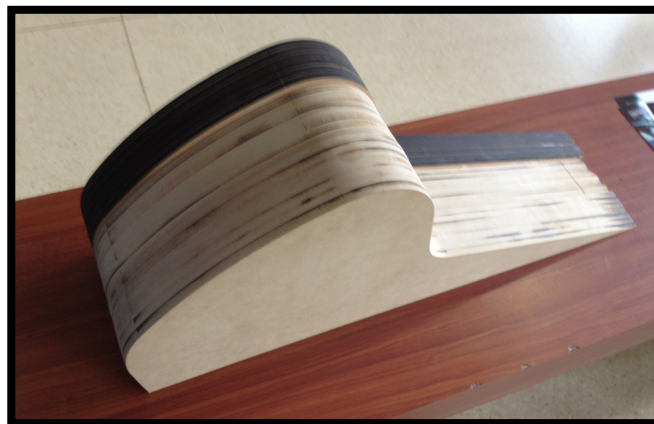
Geometría inicial del molde, con 7 piezas de aglomerado
